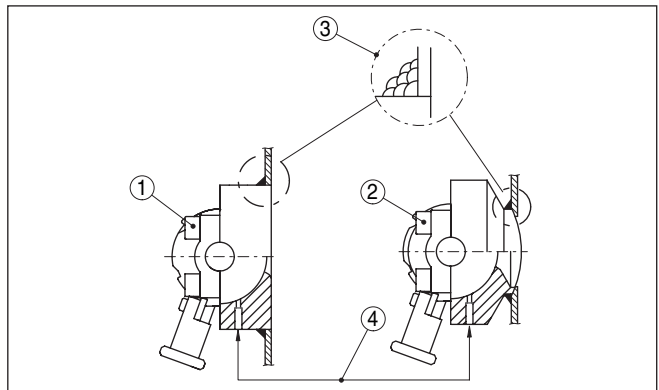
Guarnición para llave esférica PASVE en versión soldada
